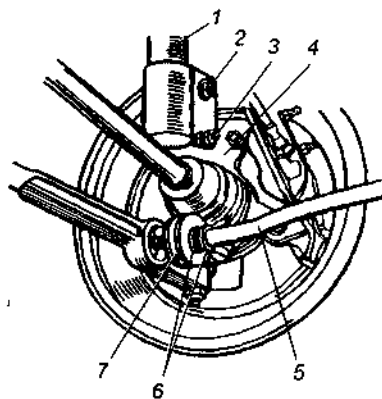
Регулировка колес автомобиля АЗЛК-2141: 1 — телескопическая стойка; 2 — болт крепления стойки к бобышке поворотного кулака; 3 — регулировочный и крепежный болт эксцентрикового ползуна; 4 — поворотный кулак; 5 — стабилизатор; 6 — шайбы регулировки продольного наклона оси поворота; 7 — опорная чашка стабилизатора
